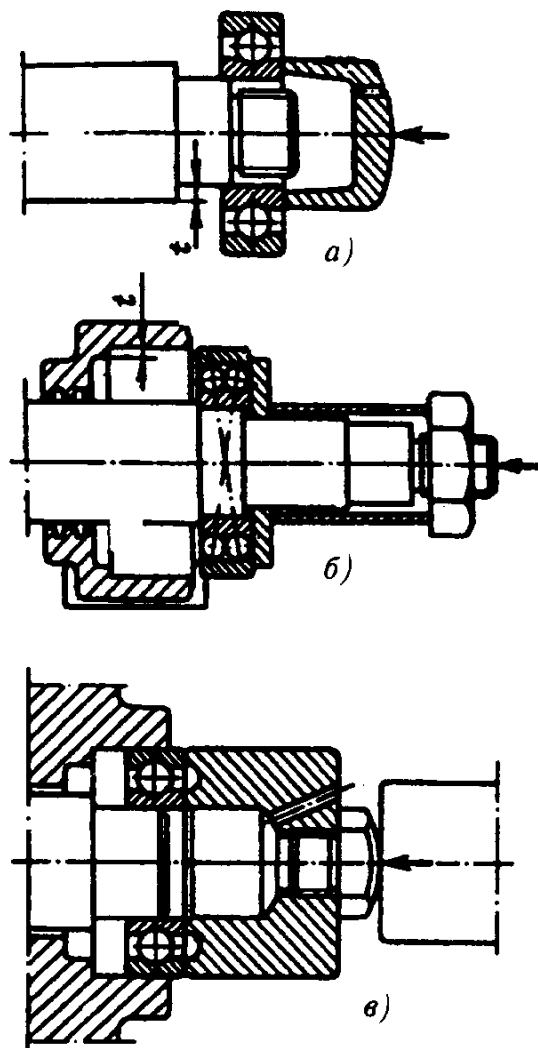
Установка подшипников на вал (а), в корпус (б), одновременно на вал и в корпус (в)
